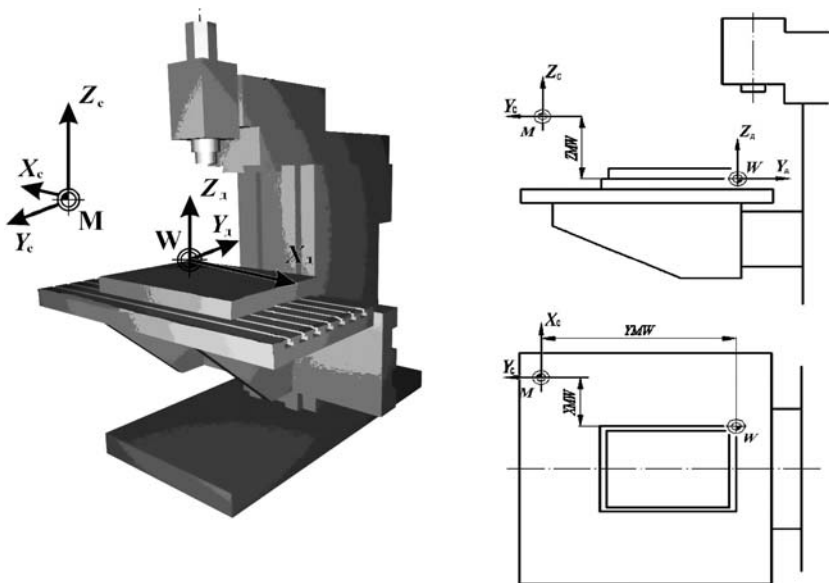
Положение нулевой точки детали W в системе координат фрезерного станка
